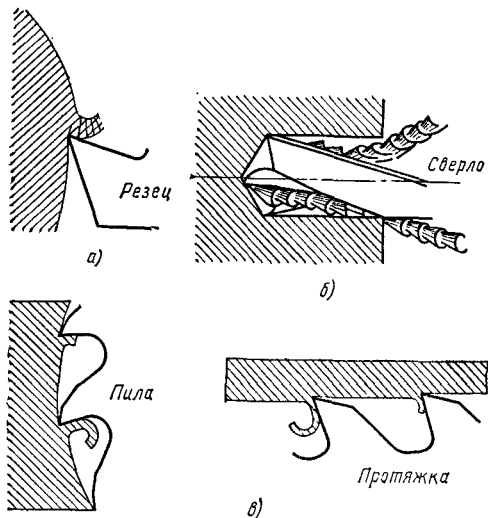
Виды размещения стружки: а — открытое пространство; б — отвод стружки при сверлении; в — закрытое пространство
